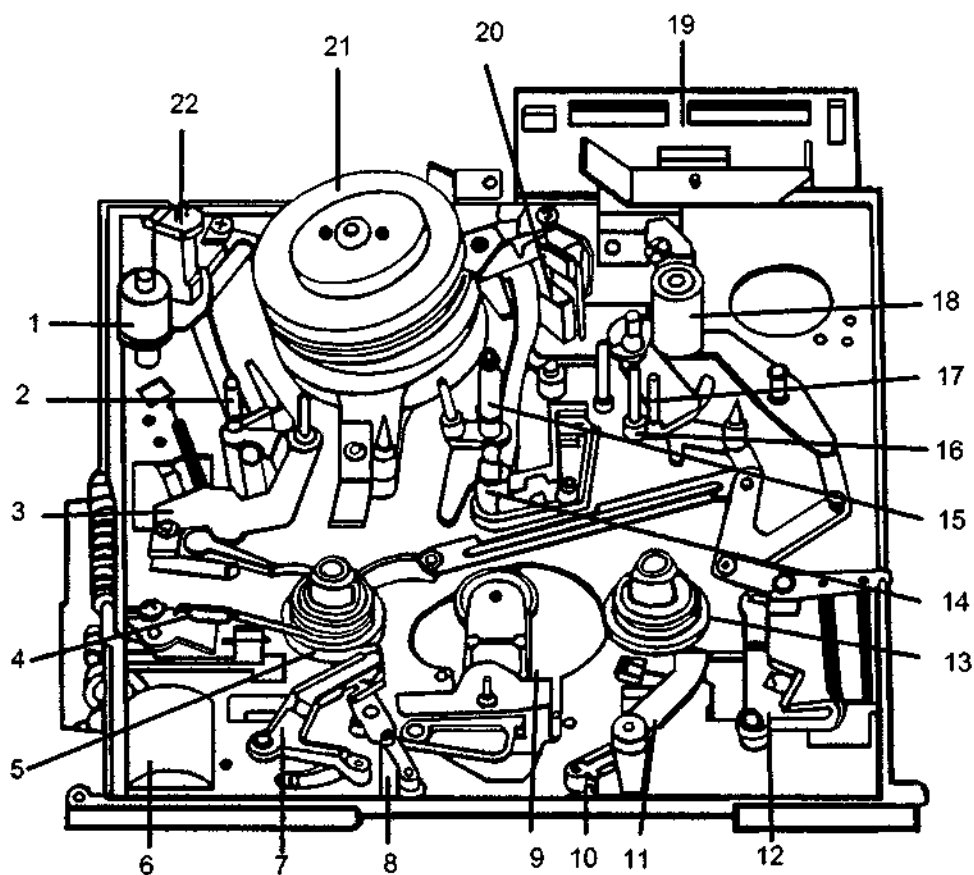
Лентопротяжный механизм (вид сверху)
